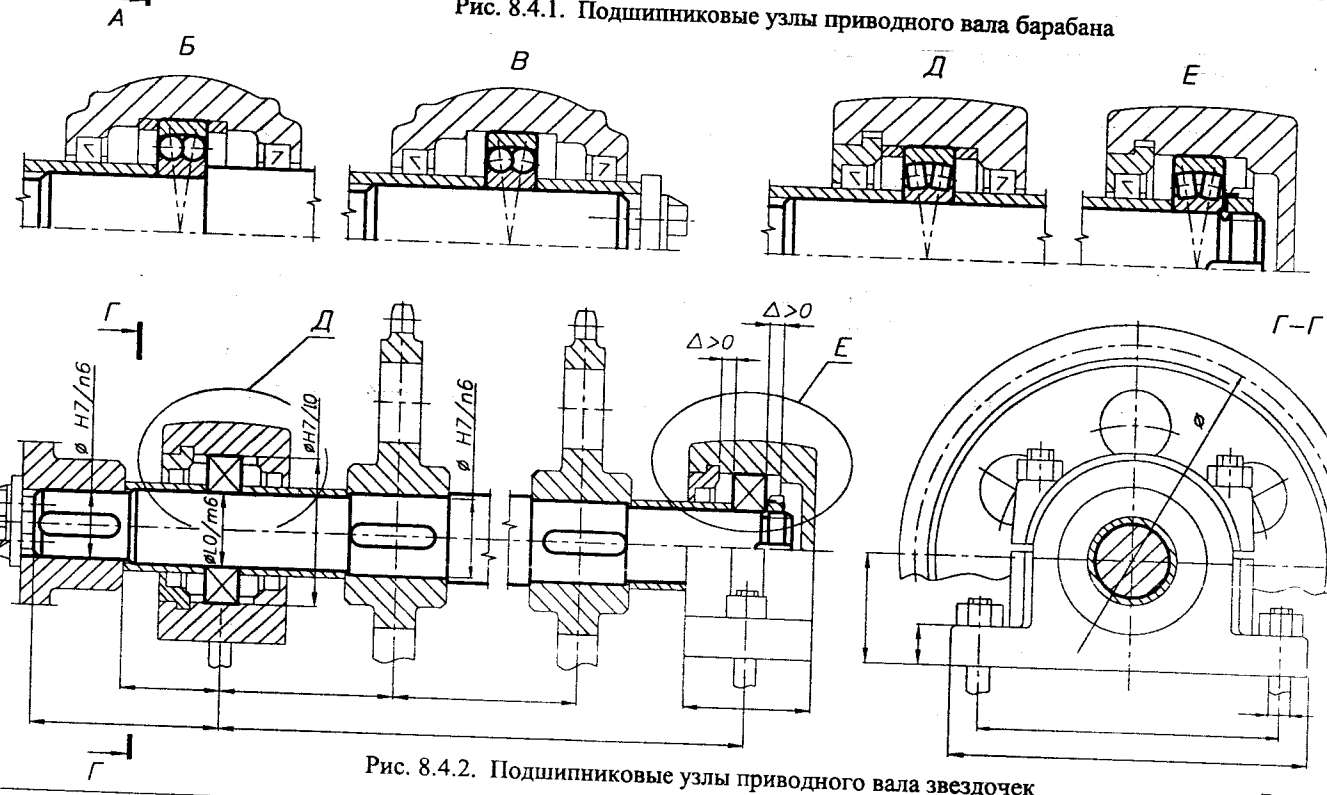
Подшипниковые узлы приводного вала звездочек
